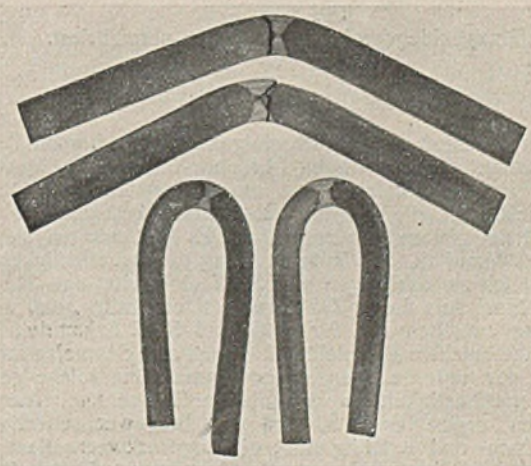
X-Naht-Verbindungsschweißung, St 48.
